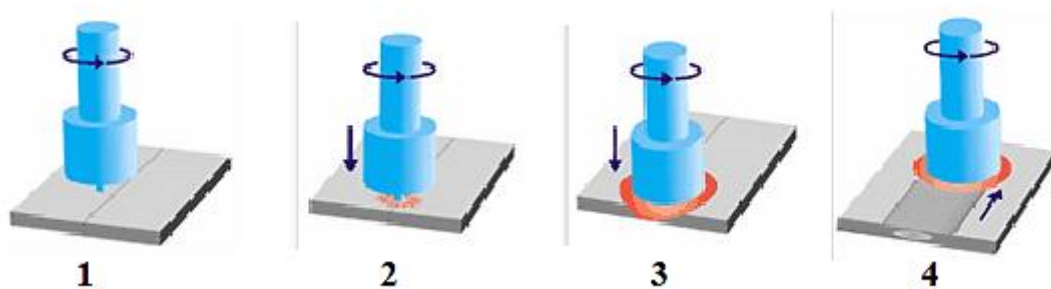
Esquema do processo de soldadura FSW.
